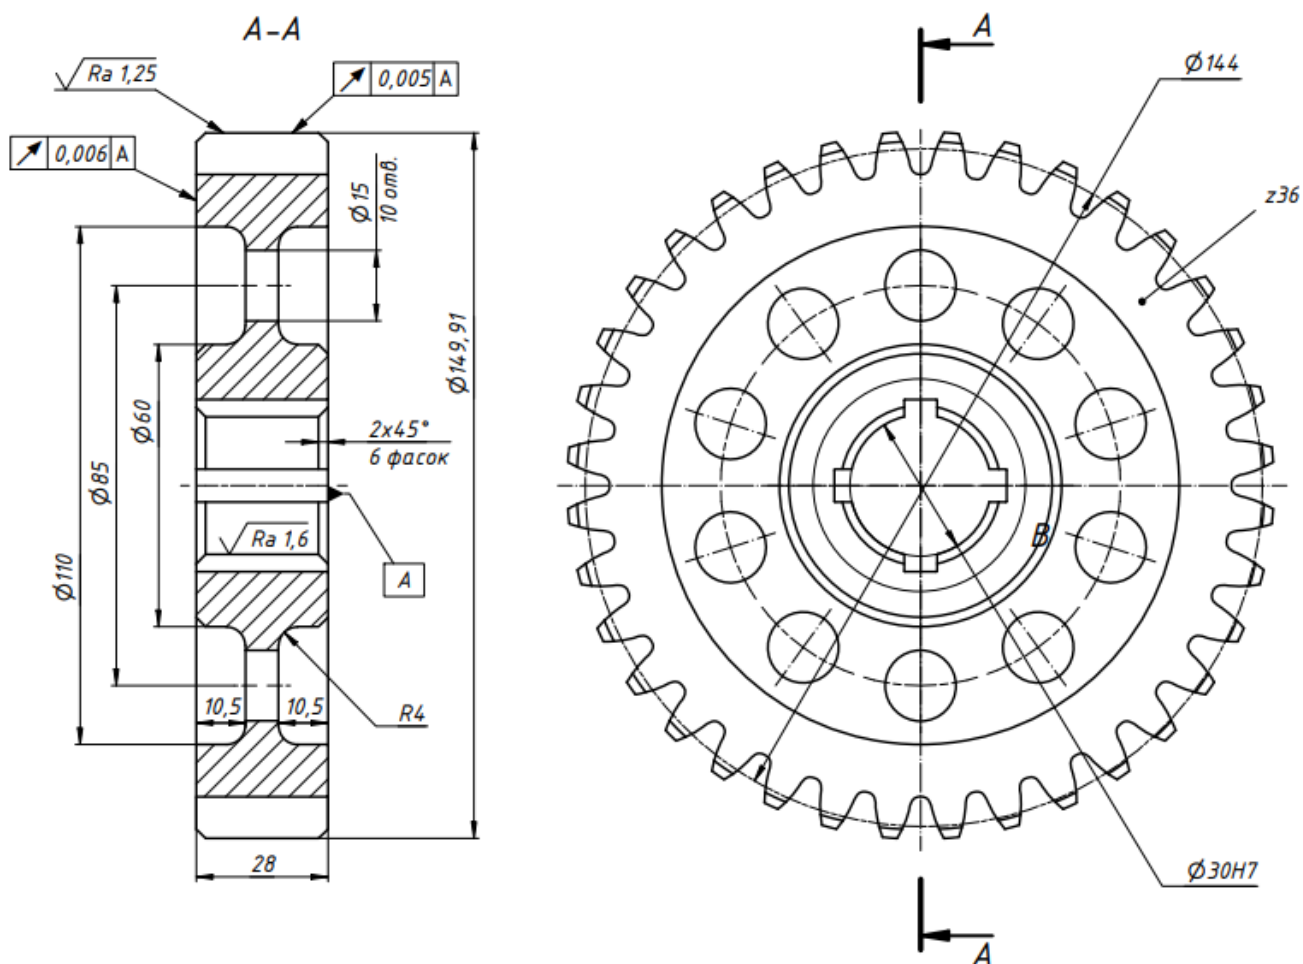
Зубчасте колесо, що регулює роботу друкарського циліндра
